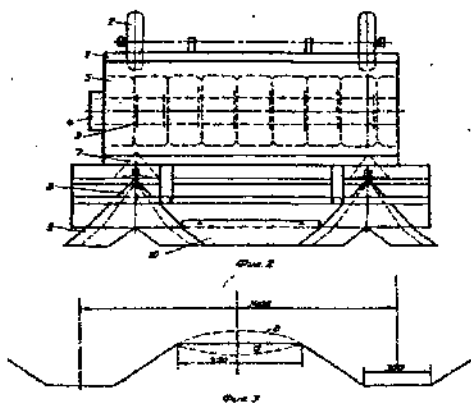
Схема фрезерного окучника – вид сверху и схема гряды после прохода орудия
